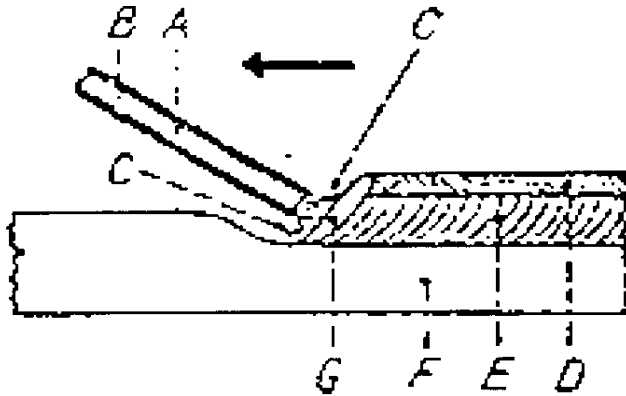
A-electrode; B-revestiment; C-gas protector; D-escòria; E-cordó de soldadura; F-metall base; G-bany de fusió
